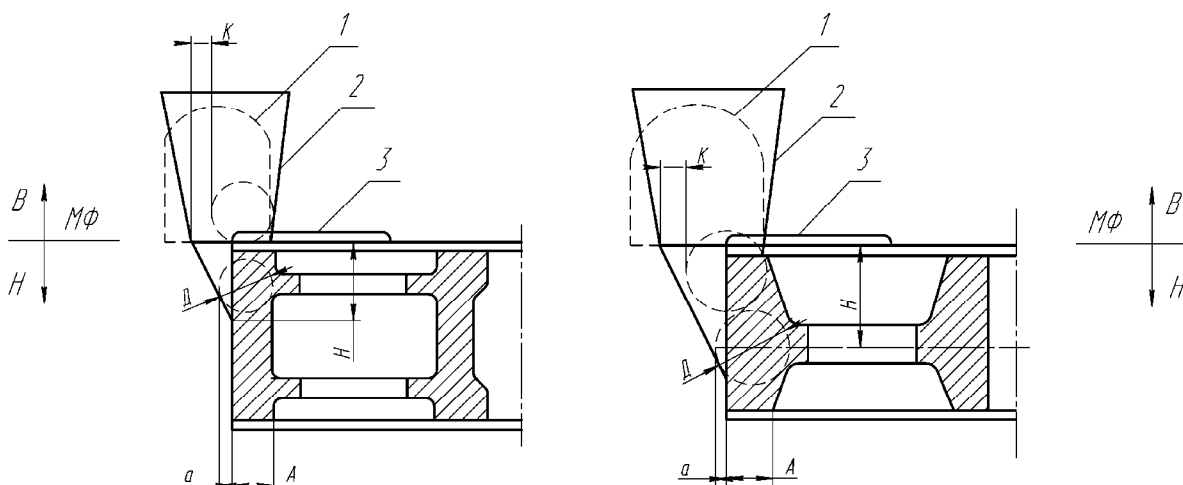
Эскиз конструирования прибыли на зубчатом колесе:
